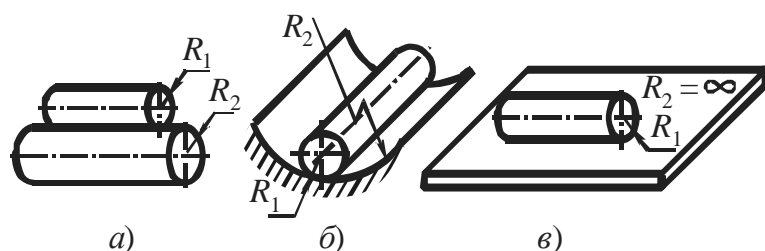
Схемы контакта деталей по линии: а) два цилиндра с параллельными осями; б) цилиндр с вогнутой поверхностью; в) цилиндр с плоскостью
